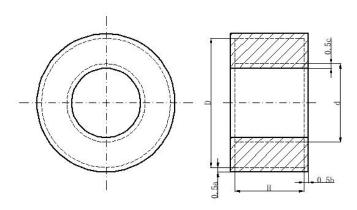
钛合金圆环类锻件机械加工余量与公差
